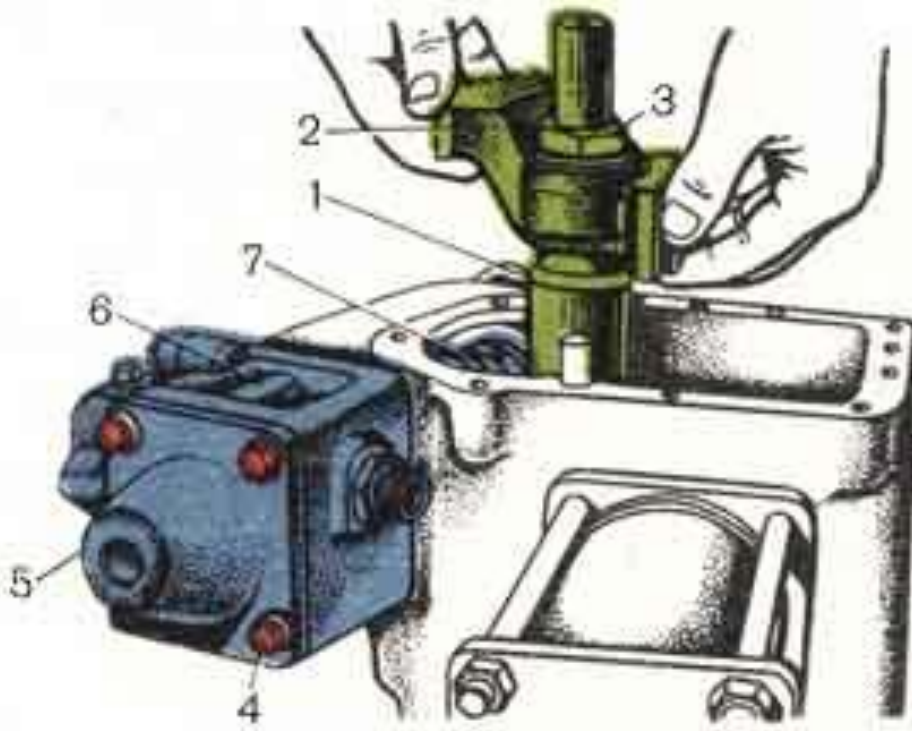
Зняття поворотного валу та черв'яка 1 – поворотний вал; 2 – сектор; 3 – гайка; 4 – болт; 5 – кришка; 6 – розподільник; 7 – черв'як.
